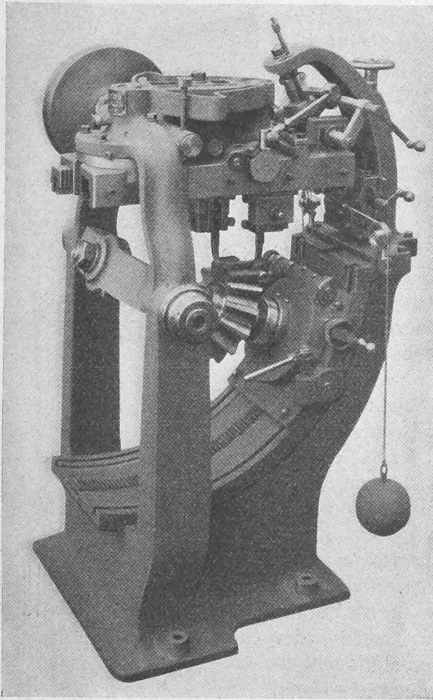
Räderhobelmaschine für Kegelräder bis 500 mm Durchmesser.
